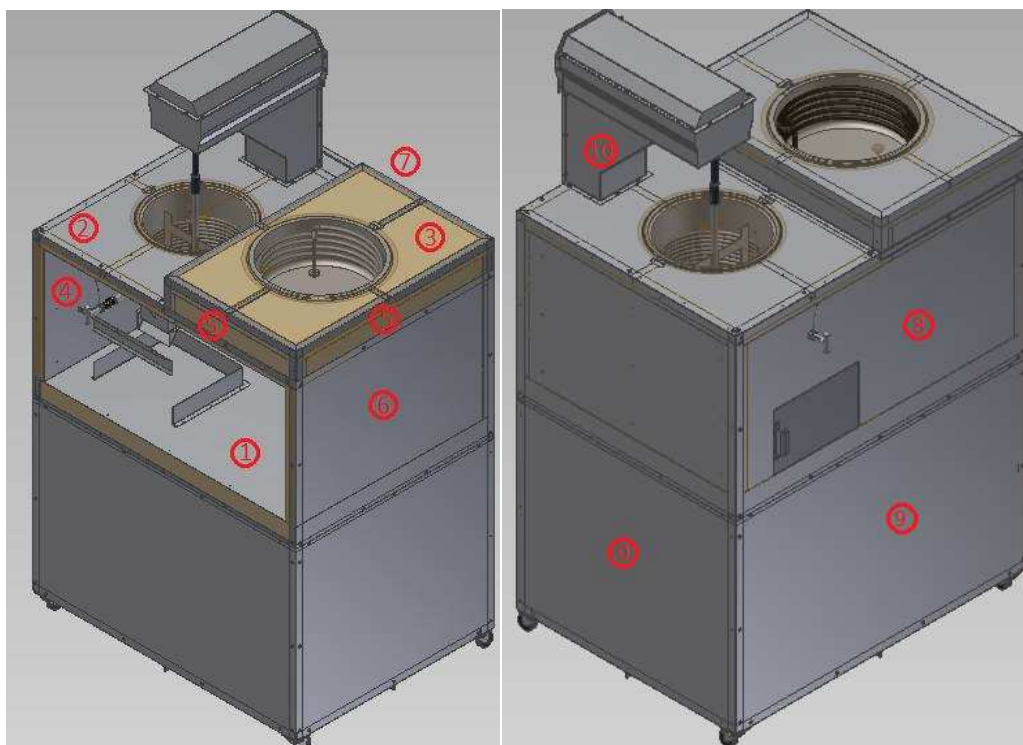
Orden de montaje de las cubiertas de la máquina.
